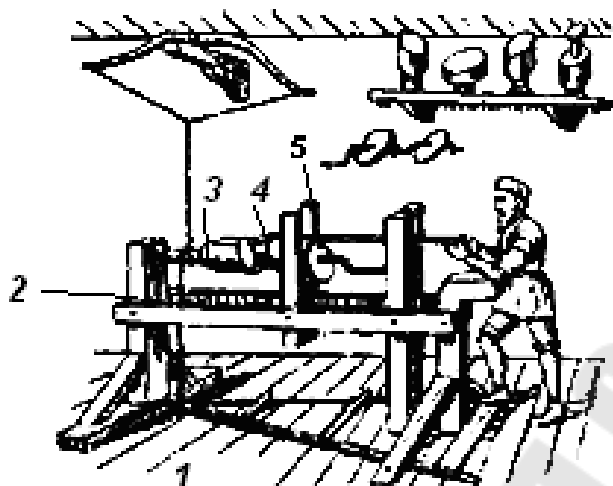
Токарно-овальверный станок (Жак Бессон 1569г.): 1 – педаль, 2 – станина, 3 – заготовка, 4 – резец, 5 – поворотный диск
